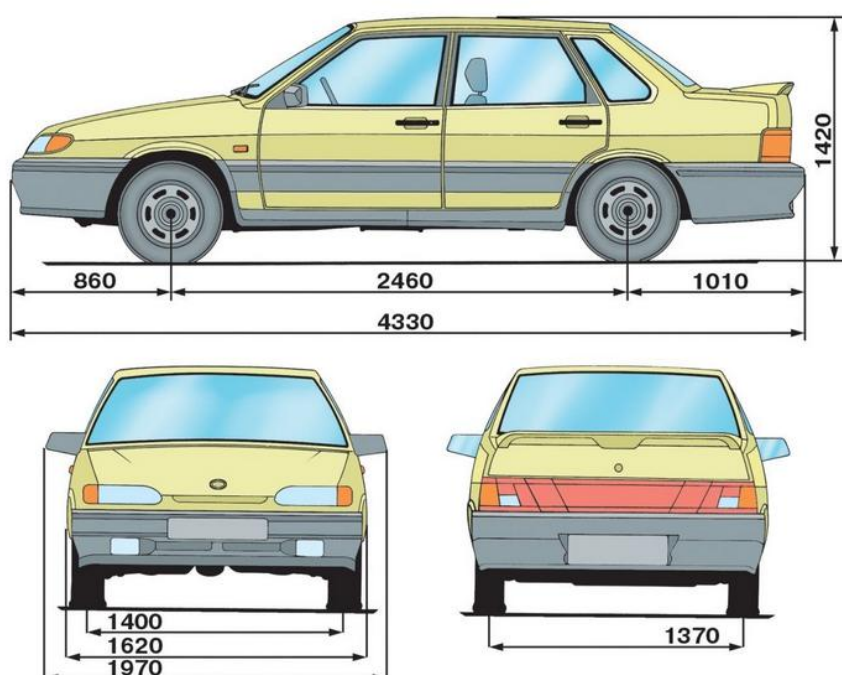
Габаритные размеры автомобиля ВАЗ–2115.
